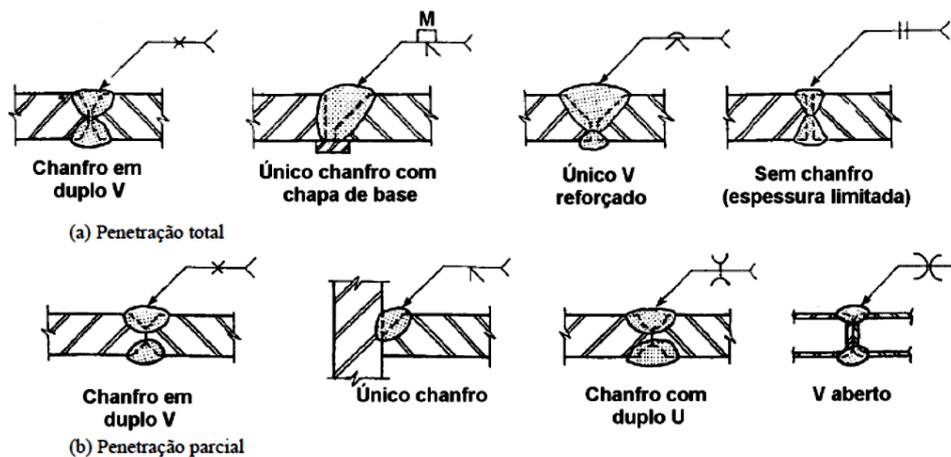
Exemplos de soldaduras de chanfro
